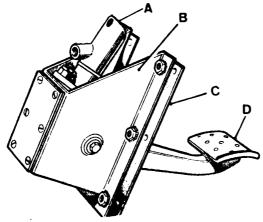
Conjunto del soporte, pedal y cilindro principal.
